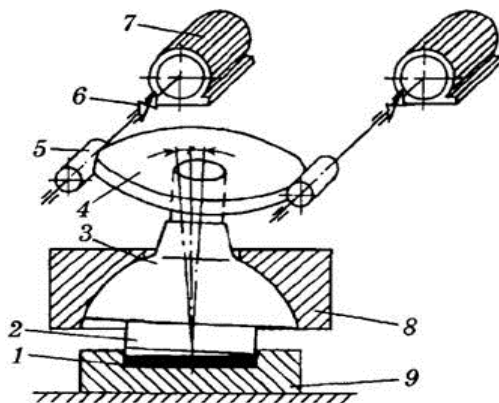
Схема конструкции сферодвижной штамповки:
